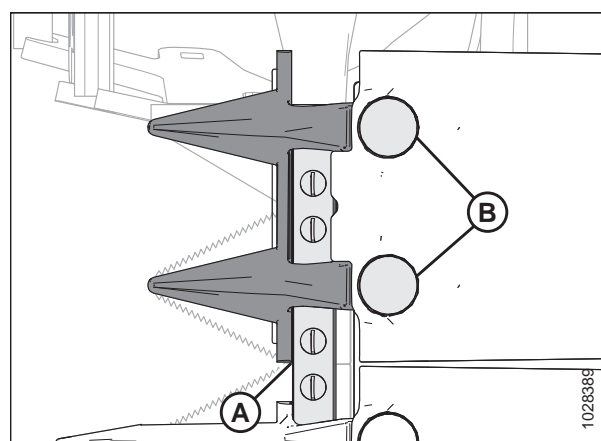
Первый противорежущий палец — вид снизу ножа
